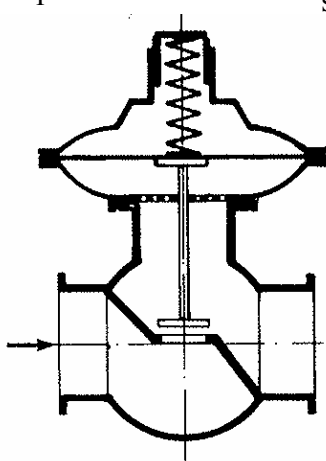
Valvola di sicurezza a membrana per gas.
